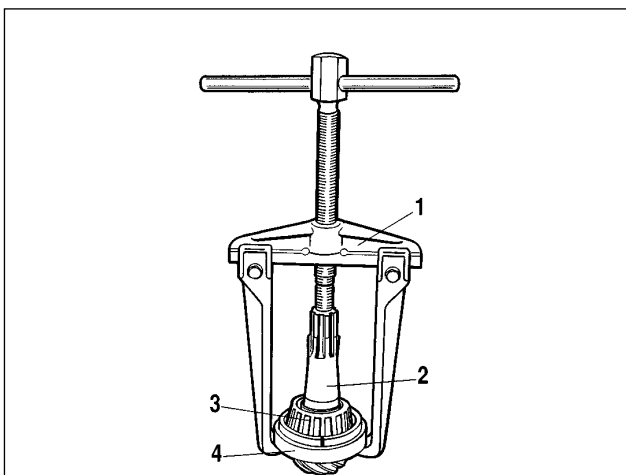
Ausbau des Innenrings des hinteren Lagers von Antriebsrad mit Universal-Abziehvorrchtung A.40005/1/7:
